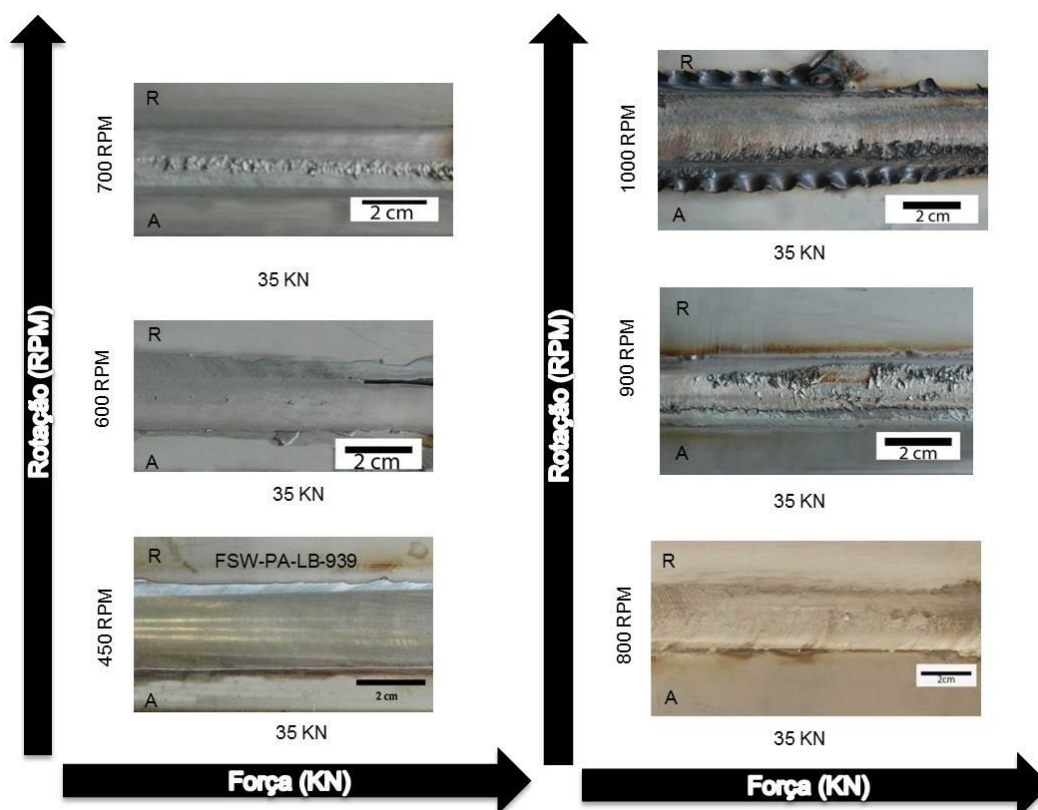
Soldagens preliminares com a variação da velocidade de soldagem no aço AISI 304L.
